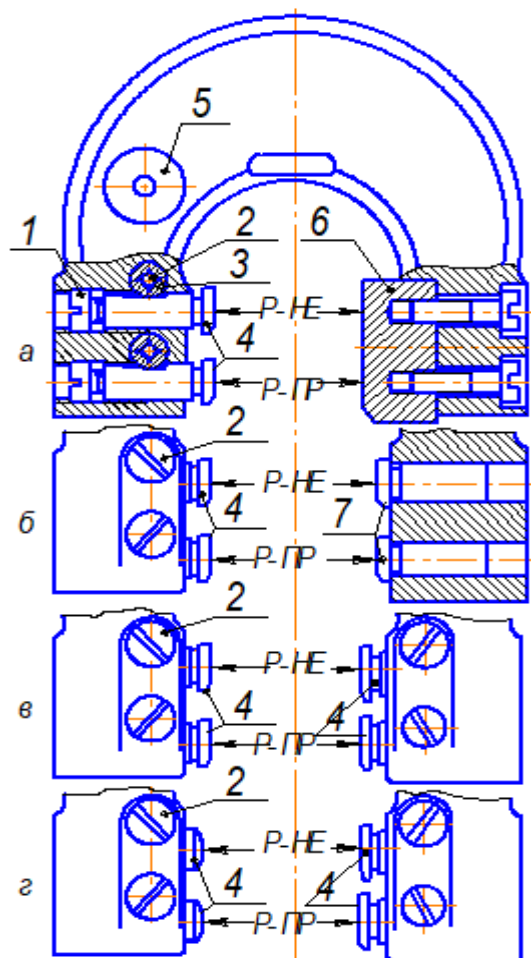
Односторонний двупредельный калибр - скоба для контроля вала $\varnothing 55h7$
